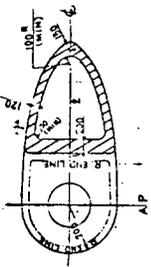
(3) 标准 STERN FRAME A0 ④ LOWER PART (BU-1)
